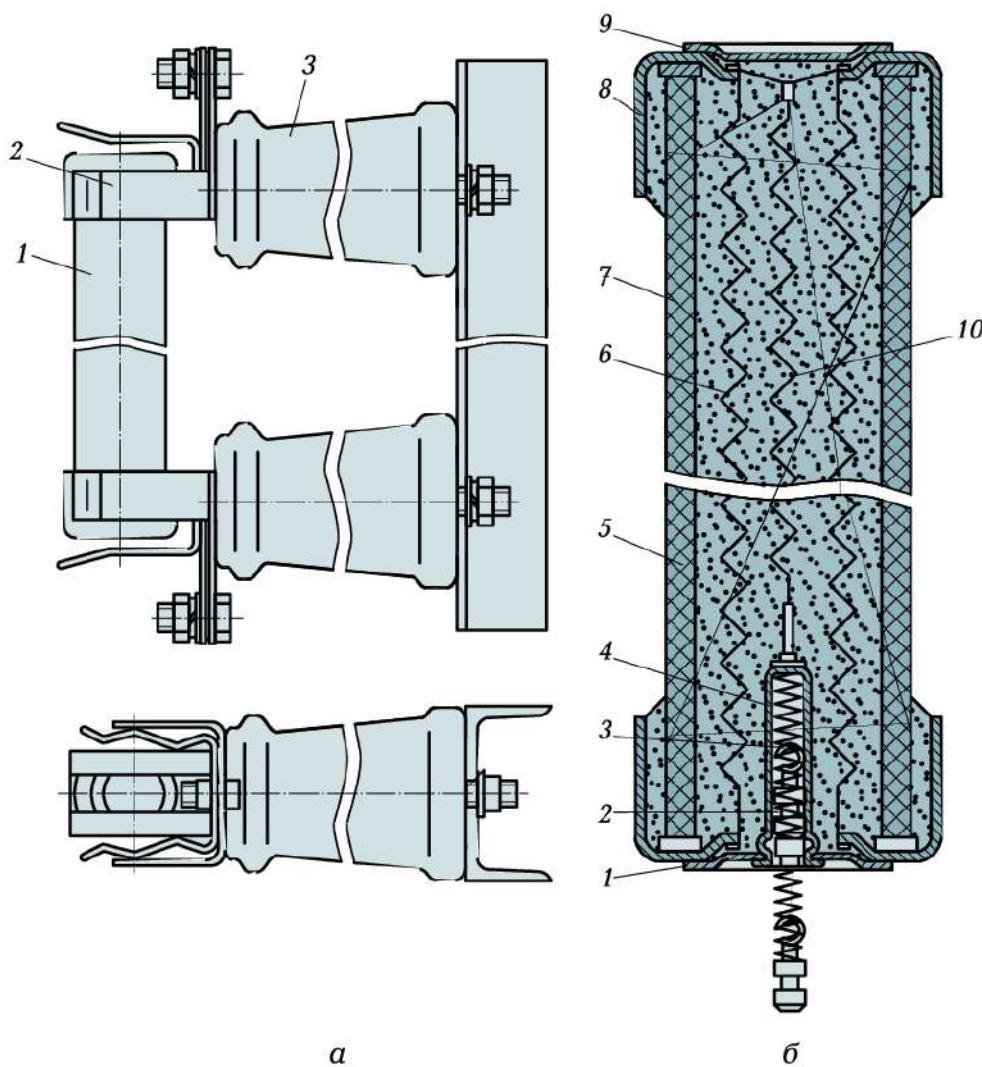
Общий вид (а) и патрон (б) предохранителя с кварцевым наполнением:
